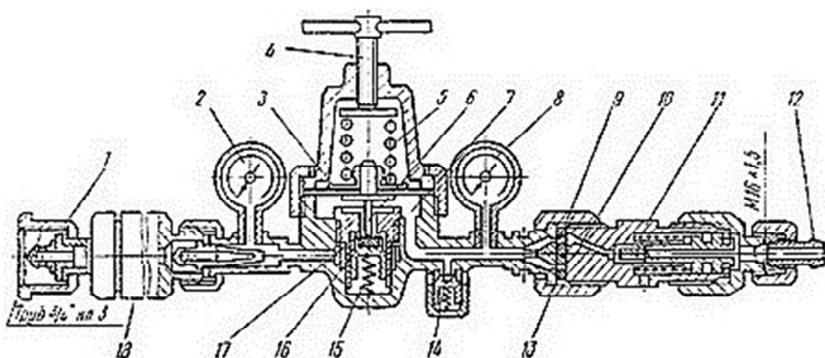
Устройство газового редуктора У-30 для углекислого газа:
